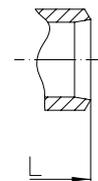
4 / 632...4 mit Schweißenden
